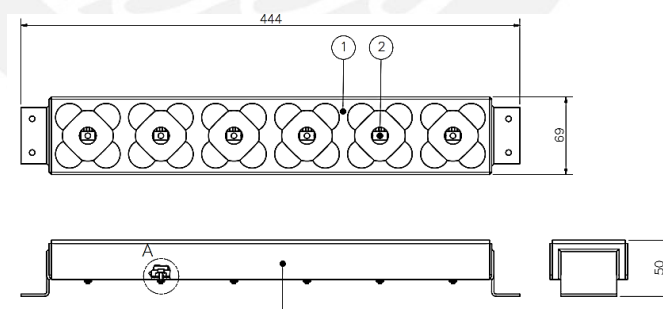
Sistema de pesado - Plano PE1.3-A3
